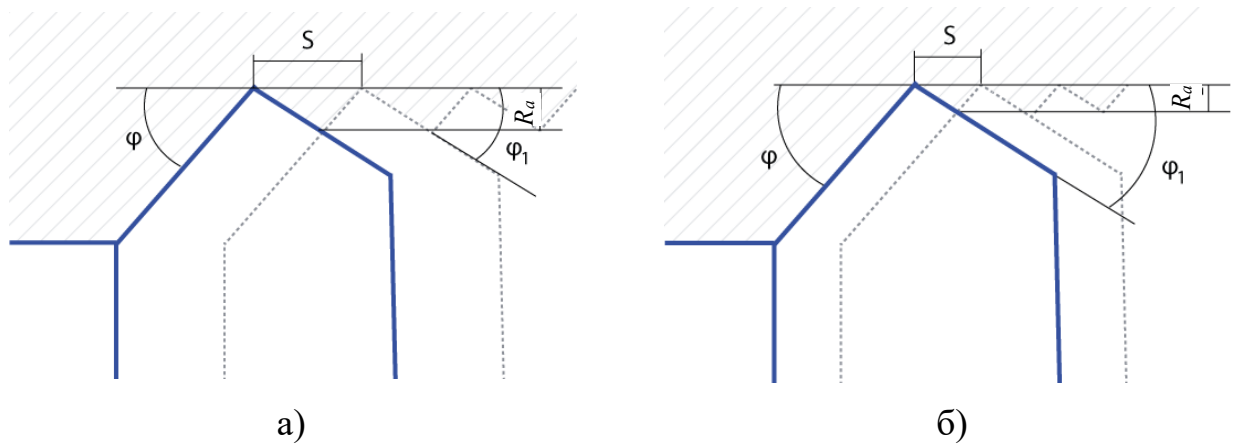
Влияние глубины резания на шероховатость обрабатываемой поверхности
